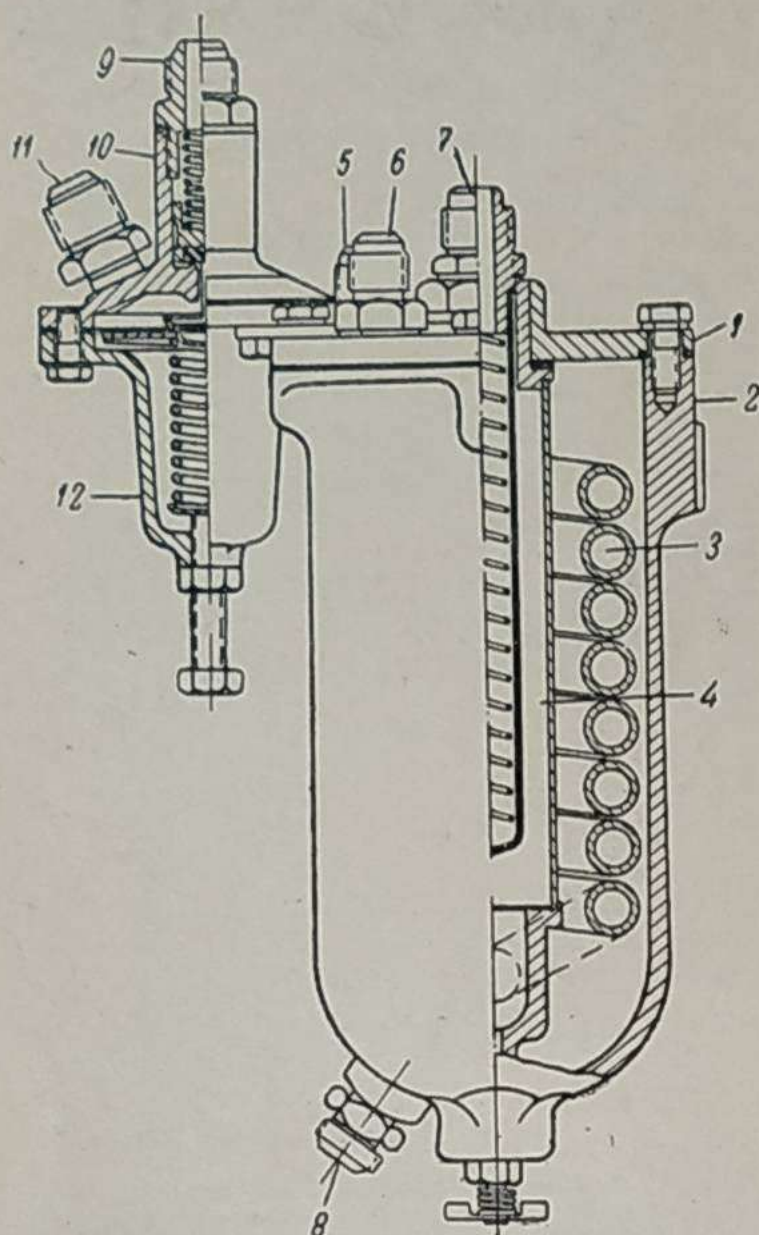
Редуктор высокого давления — испаритель: 1 — крышка испарителя; 2 — корпус испарителя; 3 — змеевики испарителя; 4 — отстойник и фильтр; 5 — входной штуцер испарителя для газа; 6 — штуцер для входа воды; 7 — штуцер для выхода газа из испарителя; 8 — штуцер для выхода воды; 9 — входной штуцер редуктора; 10 — верхний корпус редуктора; 11 — штуцер для выхода газа из редуктора; 12 — нижний корпус редуктора.
